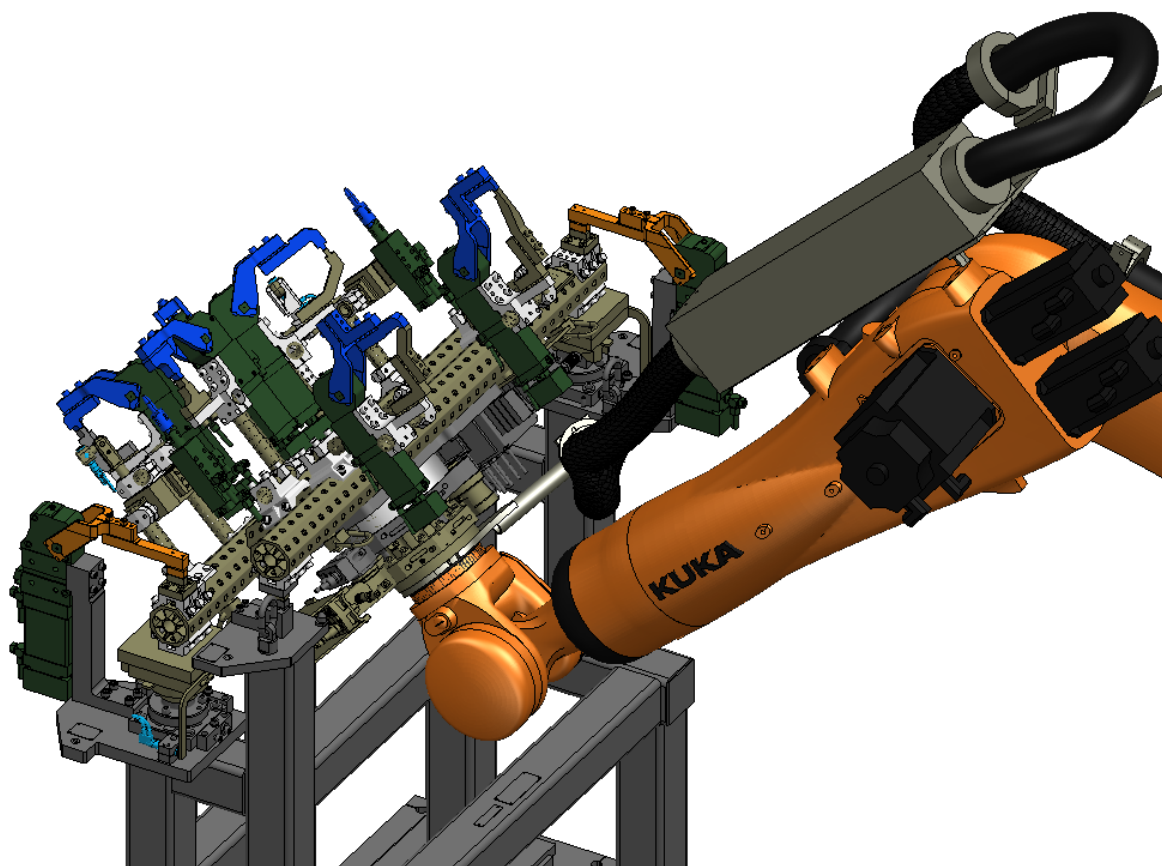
Фиксация захватного устройства передаточного робота в станции
